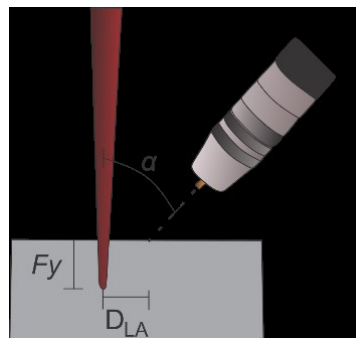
Características geométricas do posicionamento relativa entre o feixe Laser e o arco elétrico no processo de soldagem HLAW. (Fonte: Autor)
